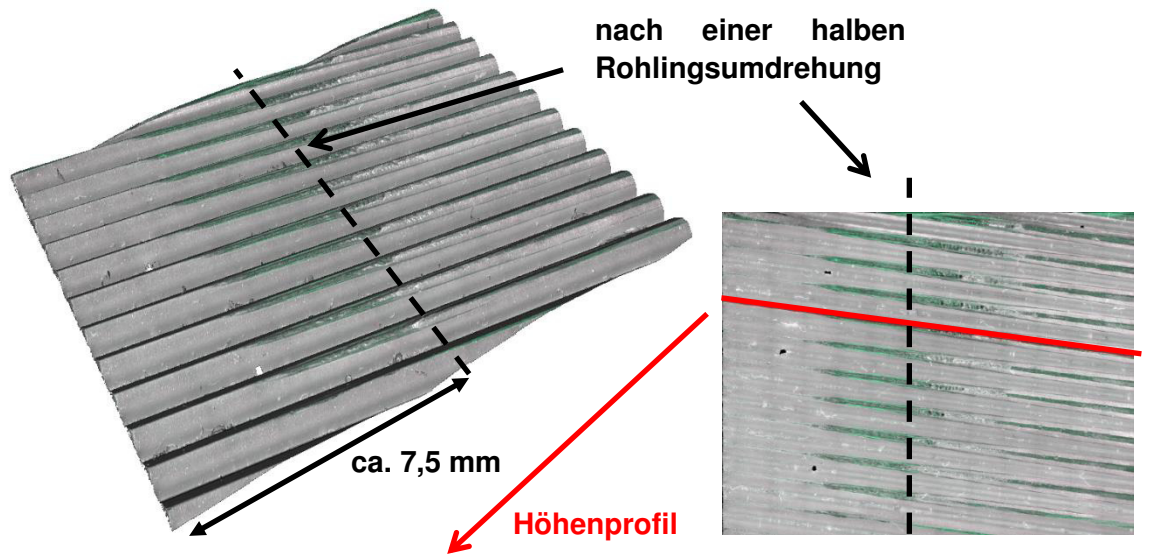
Topografie des Einlaufbereiches der langen Walzbacke (nach 715000 gewalzten Schrauben)
